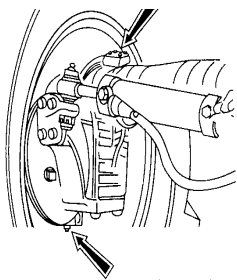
Смазка подшипников опор шкворня колесного редуктора и втулок оси качания переднего ведущего моста
